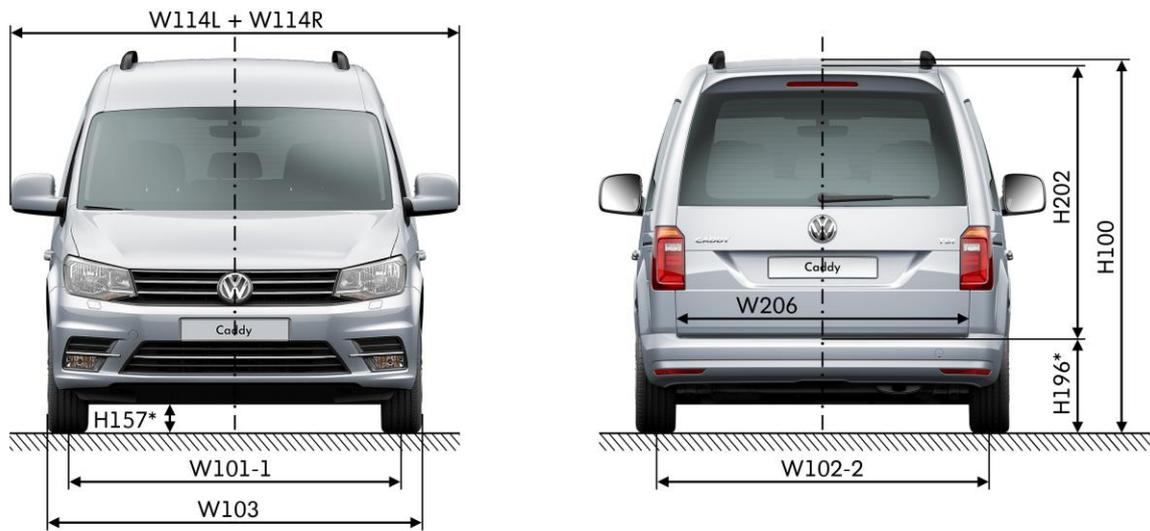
Cotes du Caddy/Caddy Maxi, vue de devant et de derrière (conformément à la norme DIN70020, partie 1)
